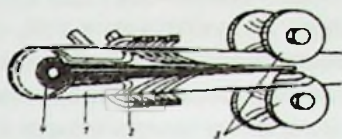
Схема индуктивного токоподвода при непрерывной высокочастотной стыковой сварке:
